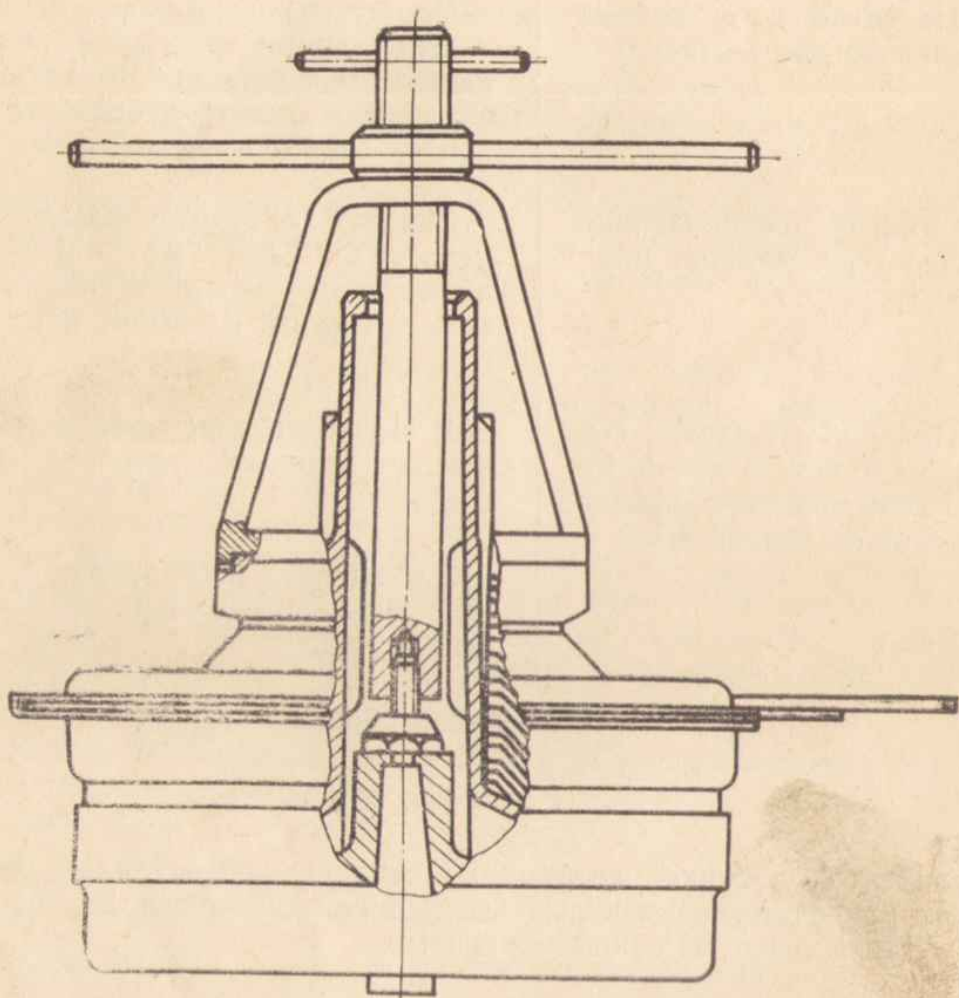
Схема работы приспособления для сжатия пакета тарелок барабана.
